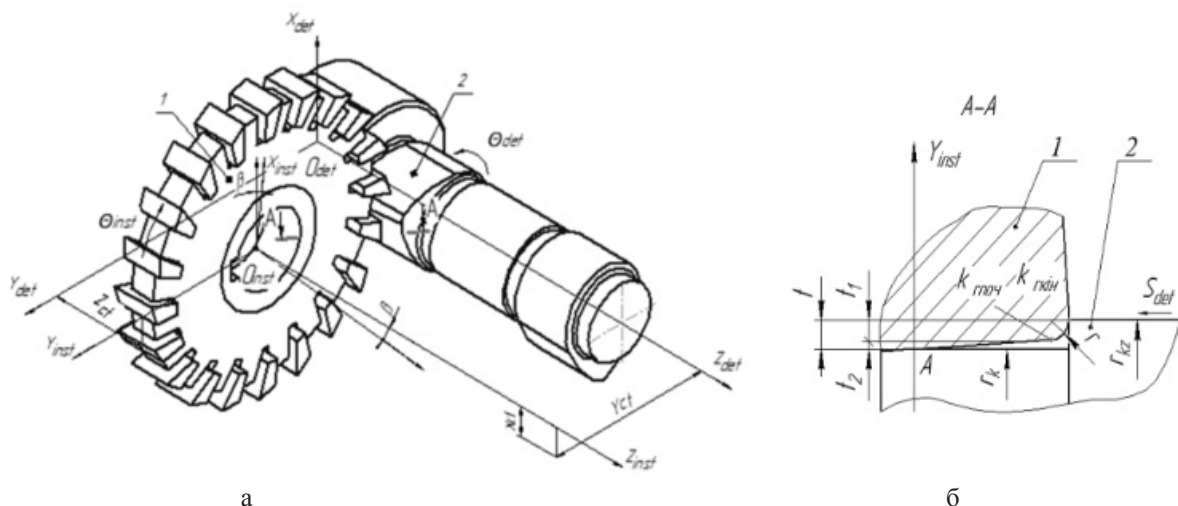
Фрезерування розподільного вала зі схрещеними осями інструмента й деталі
